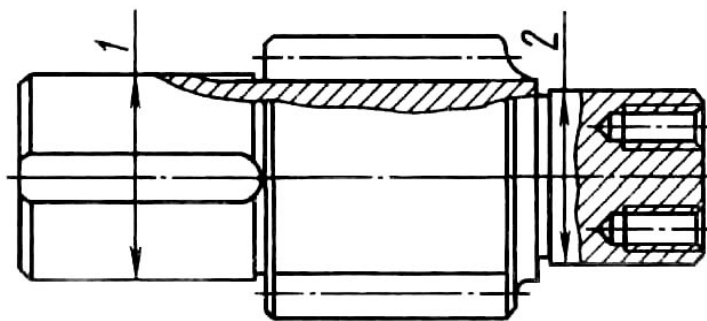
Расположение шеек ведущей цилиндрической шестерни:
